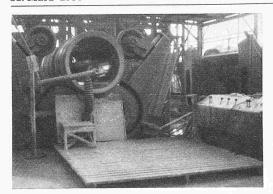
Anlage zur Herstellung der 5 m langen Betonrohre
